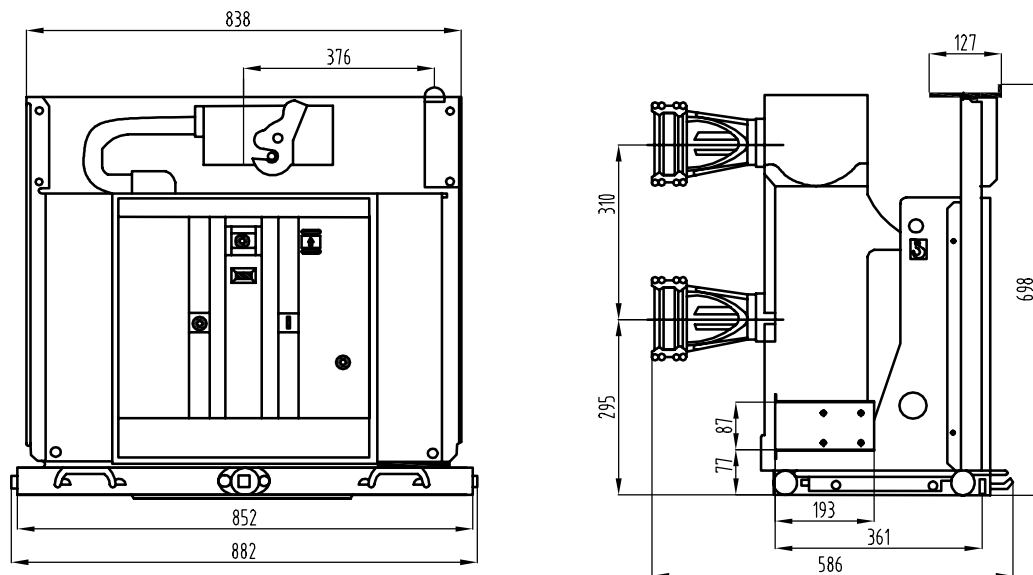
Габаритный размер выключателя ВВ-12 выкатного исполнения для ячейки шириной 1000 мм
